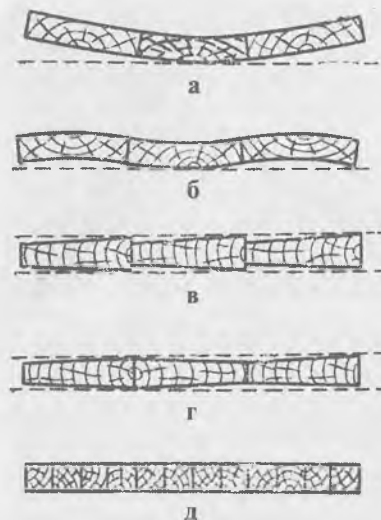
Коробление клееных щитов из массива древесины, набранных из делянок с различным расположением волокон и направлением годовых слоев древесины:
